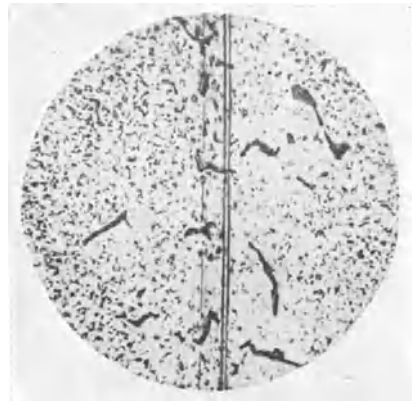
Gefüge der Stumpfschweißung
